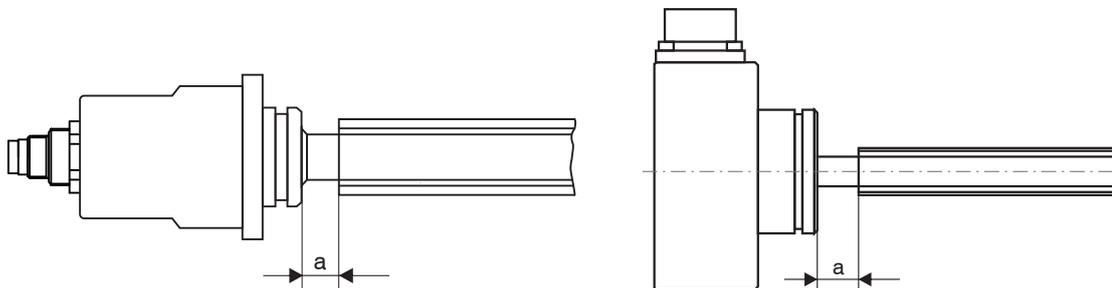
Position point zéro du tube de mesure, EDS- ... -S Fig. 3 Position point zéro du tube de mesure, EDS-...-F
